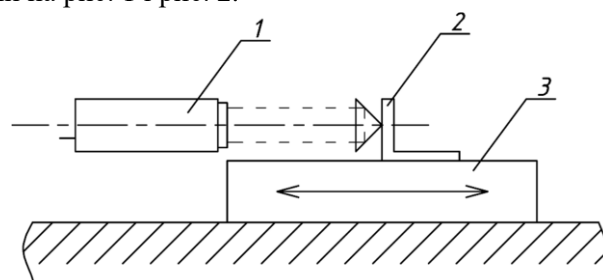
Схема контролю прямолінійності переміщень робочих вузлів верстата з використанням лазера: 1 – лазер; 2 – фотоприймач; 3 – контрольований робочий вузол
